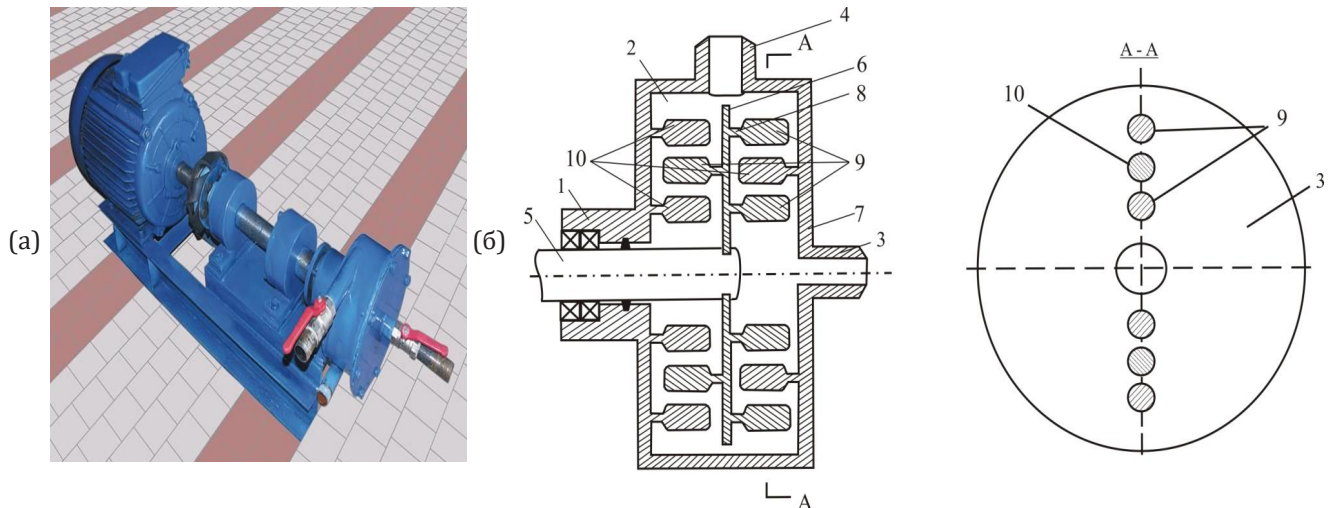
Роторный гидродинамический генератор кавитации: (а) – общий вид, (б) – принципиальная схема: 1 – корпус; 2 – рабочая камера; 3 – входной патрубок; 4 – выходной патрубок; 5 – вал двигателя; 6 – диск; 7 – торцевая стенка рабочей камеры; 8 – обтекаемая стойка цилиндра; 9 – подвижные цилиндры; 10 – неподвижные цилиндры.
